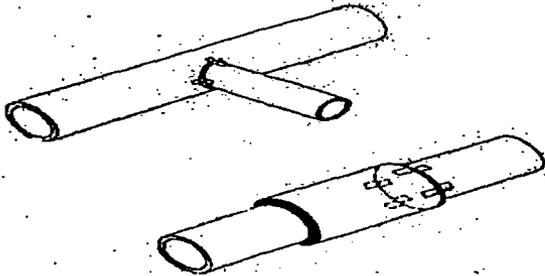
ENSAYO PARA CALIFICACIÓN MÚLTIPLE DE SOLDADOR
